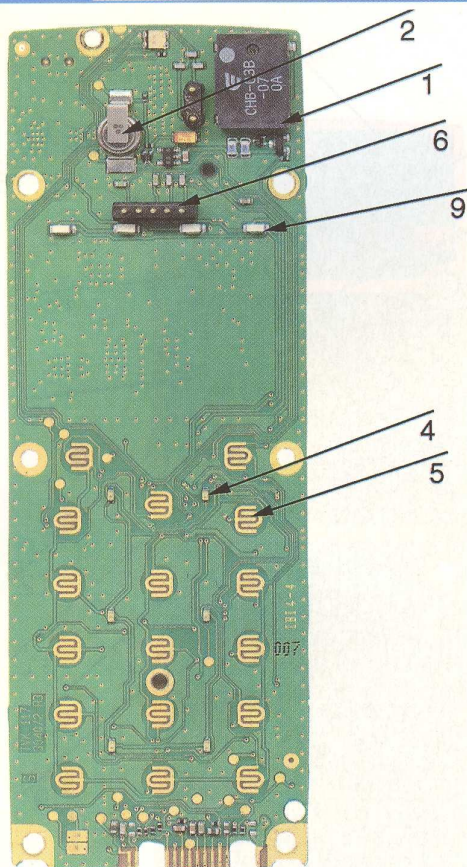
PCB echipat la modelul A1018, fața 2 (cu display)
